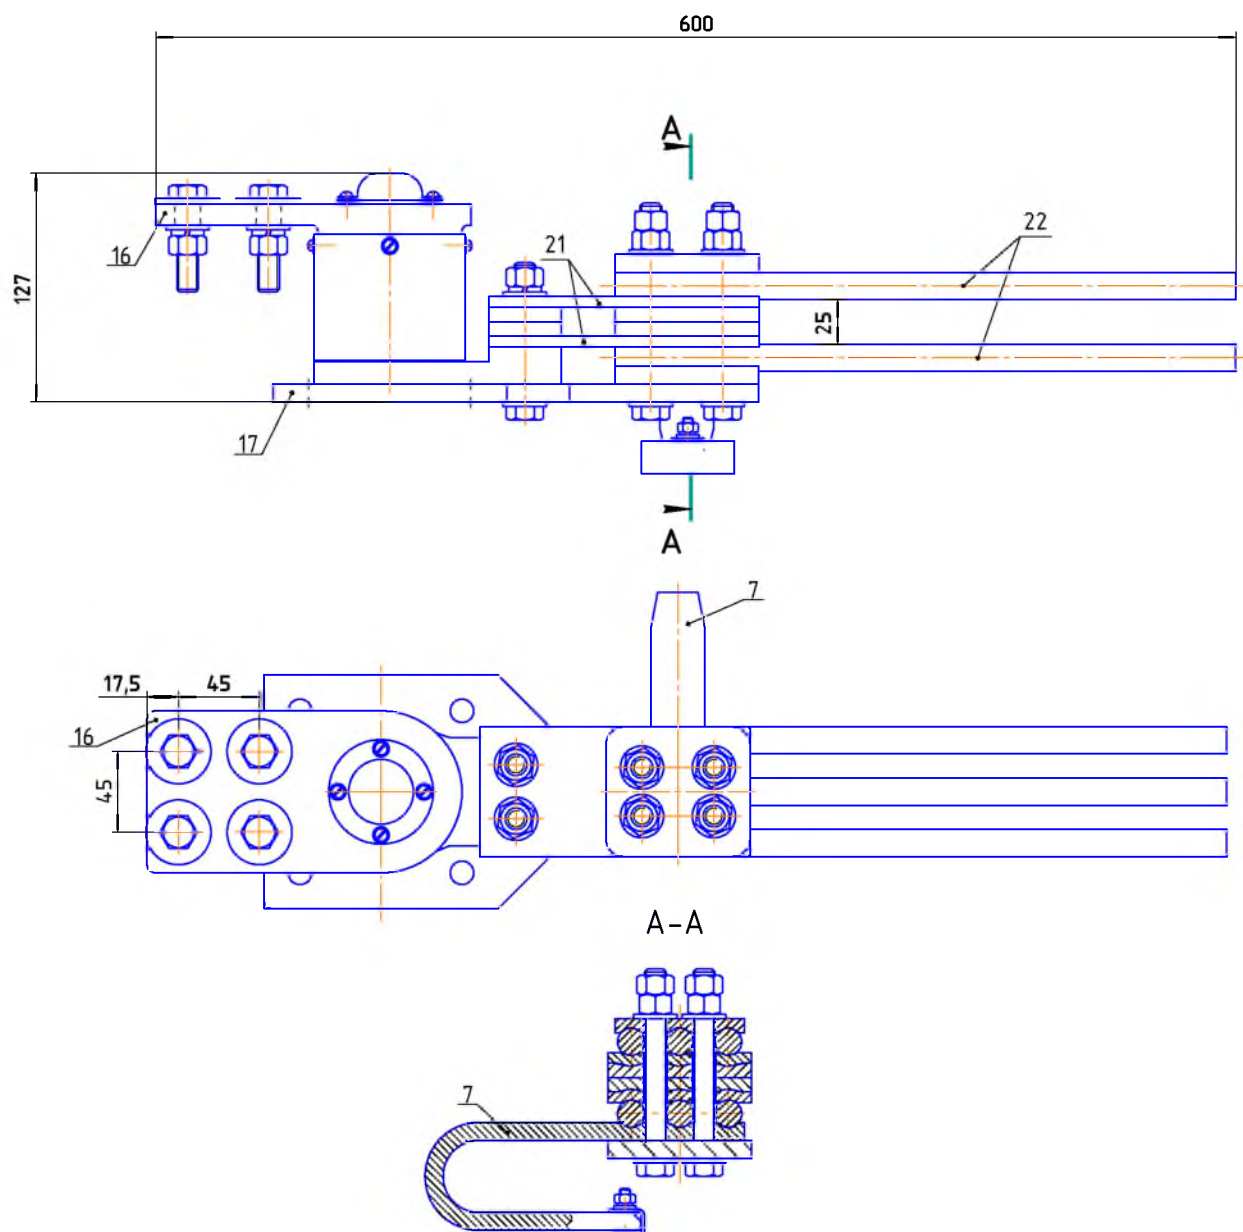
Подвижный нож контактный разъединителя РГП СЭЩ®-35/2000
